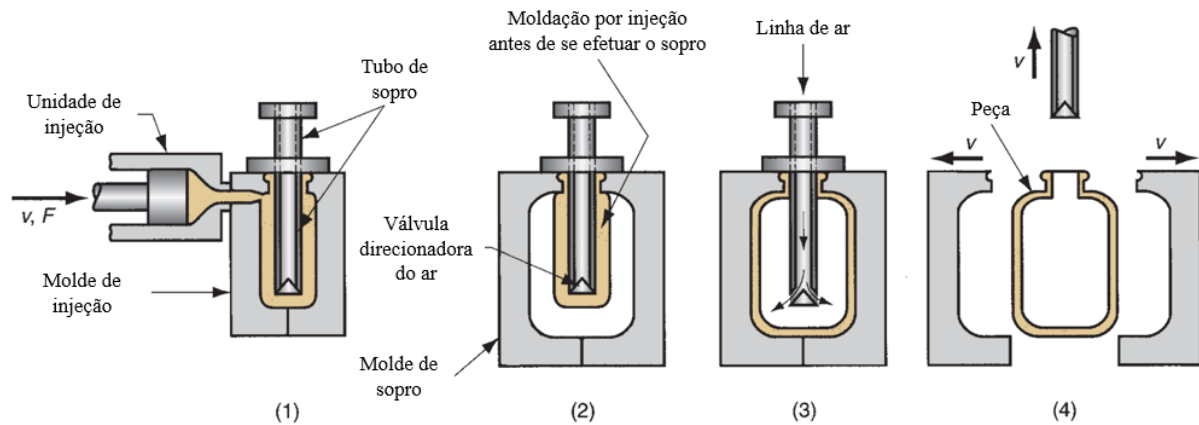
Esquema representativo do processo de moldagem por insuflação (Adaptado de [57]).
